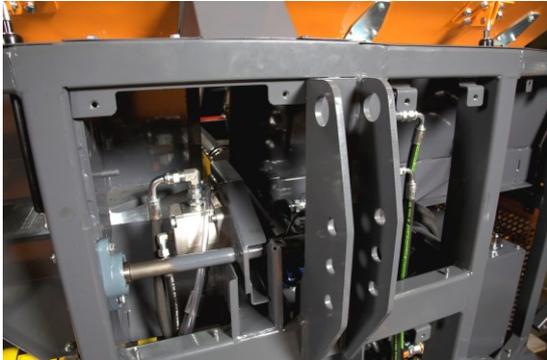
Lager des Flansches in der Schneidanlage 2 Stücke
